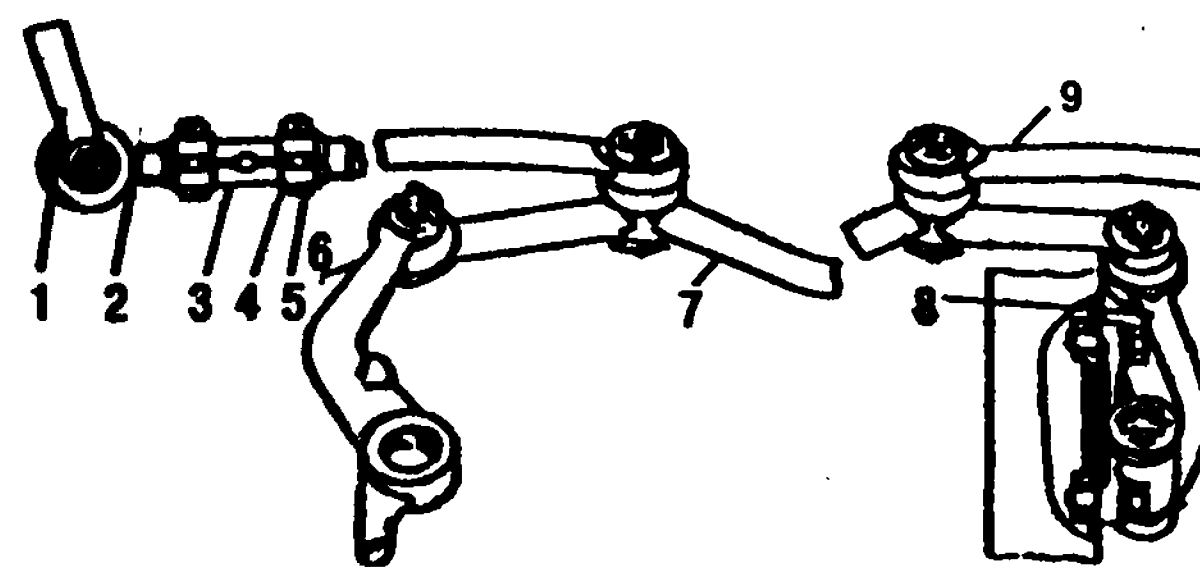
Рулевые тяги: 1 - рычаг поворотного кулака; 2 - наконечник тяги; 3 - регулировочная трубка; 4 - стяжной хомут; 5 - болт; 6 - сошка; 7 - тяга сошки; 8 - маятниковый рычаг; 9 - боковая тяга
